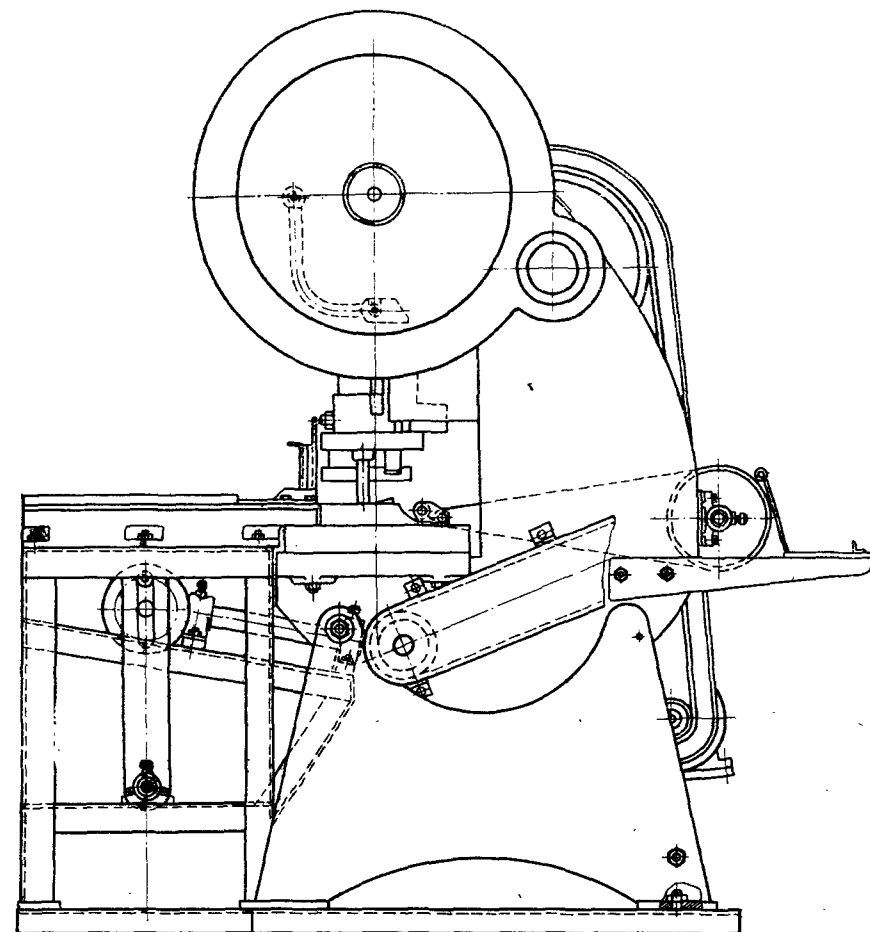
Штамповочный станок-полуавтомат для разрубки технологически двойных пластин стартерного типа
